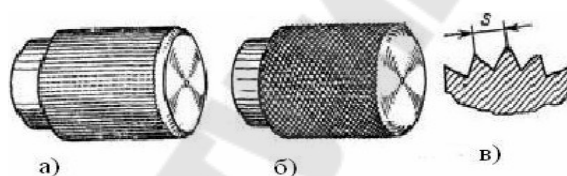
Схема накатки рифленых поверхностей: а – прямая; б – сетчатая; в – шаг накатки
